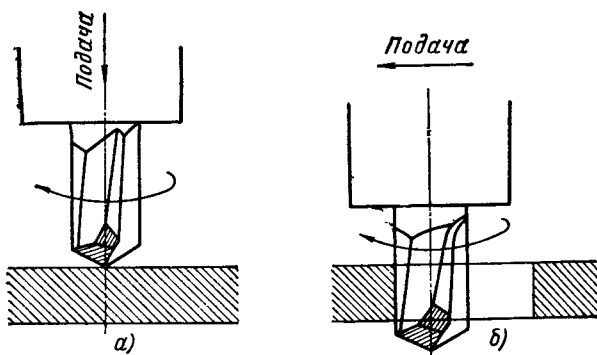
Схема работы сверла-фрезы для овальных отверстий:
